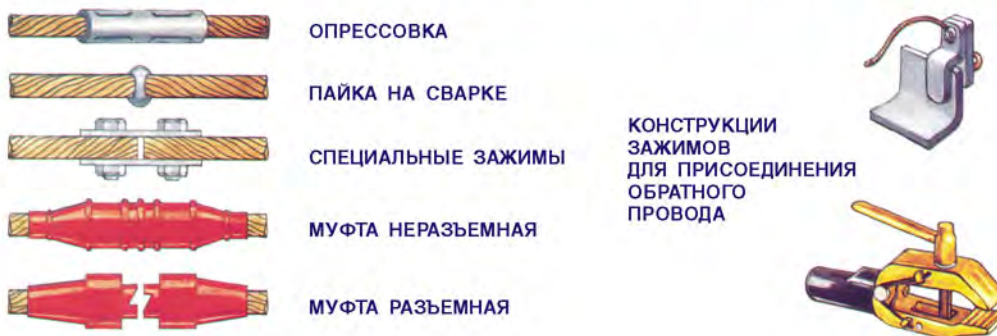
Электробезопасность при ручной дуговой сварке
